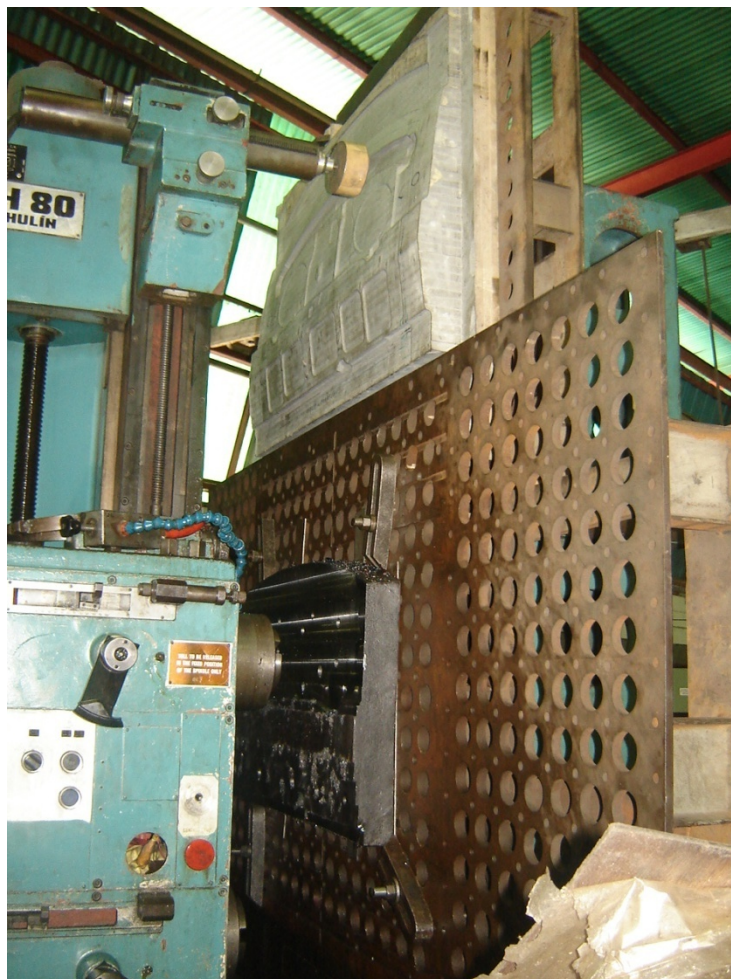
Desbaste inicial en la máquina copiadora del macho estampador
